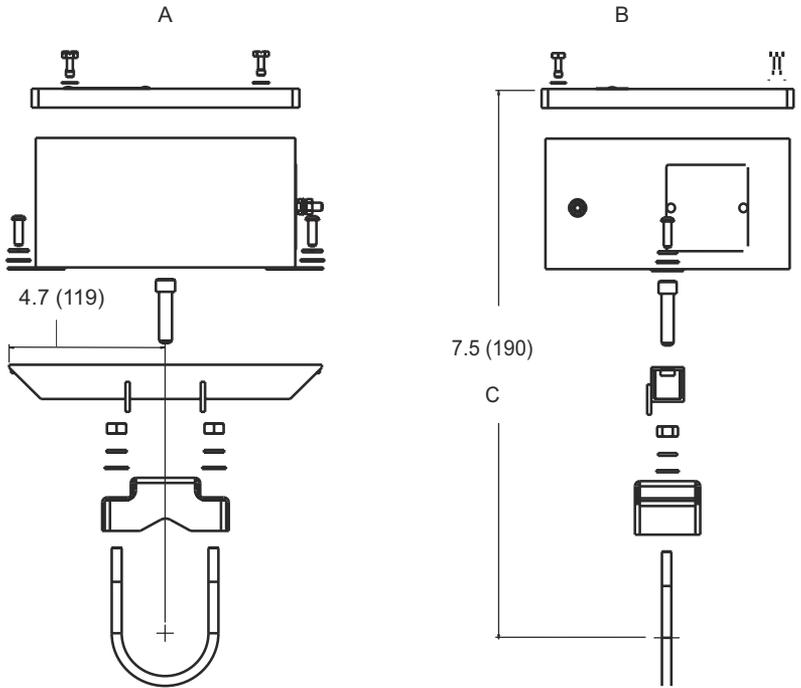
Montaje de una caja de conexiones de aluminio
